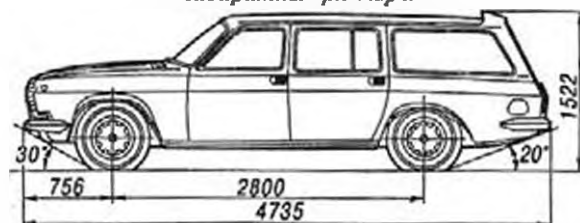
Автомобиль ГАЗ-24-12 "Волга" и его габаритные размеры
